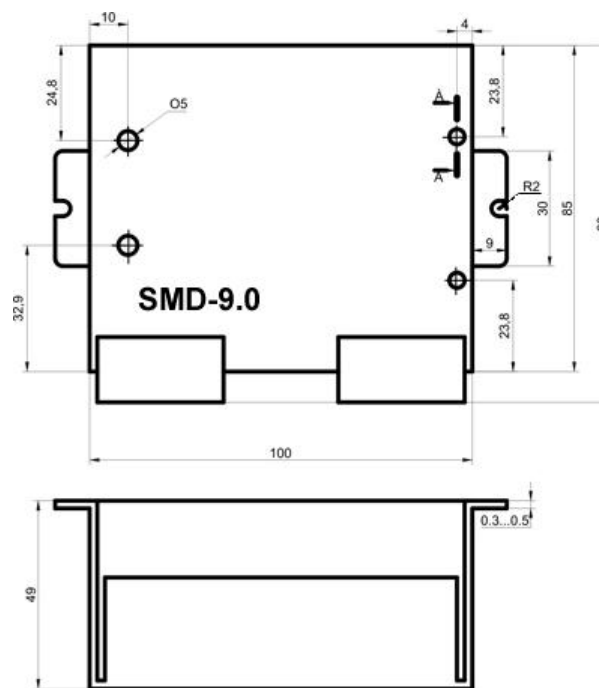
Габаритные размеры блока управления SMD 9.0.
